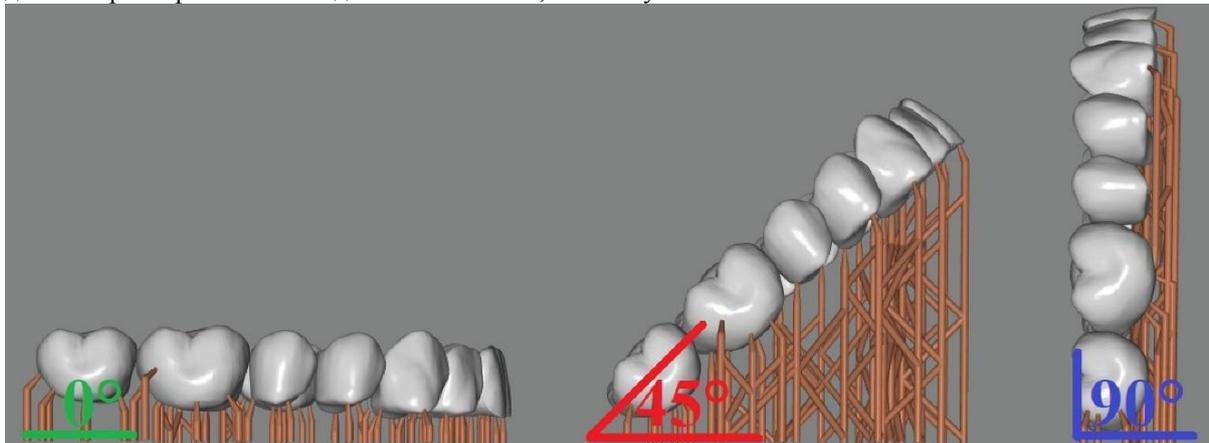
Схема трех различных направлений печати 0° , 45° и 90°
